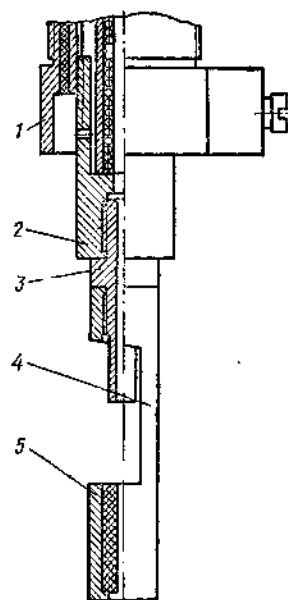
Схема усовершенствованной приставки к держателю для сварки с увеличенным вылетом:
